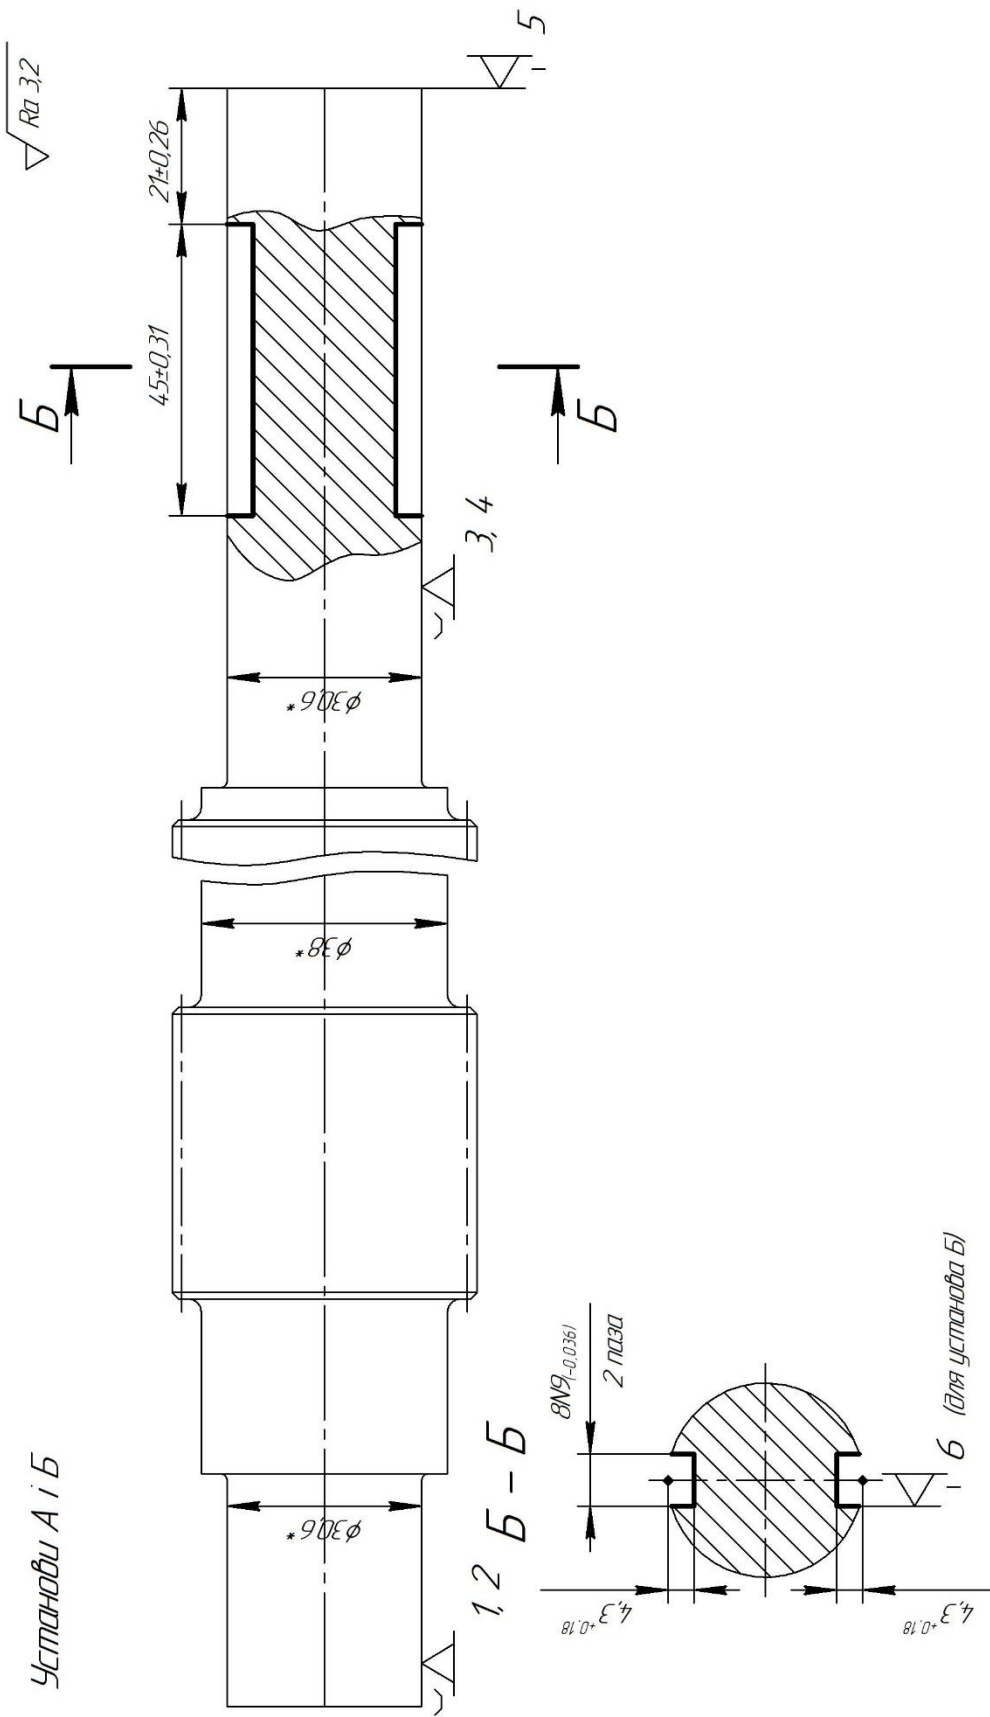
Схема базування заготовки на операції 040 фрезерній з ЧПК
